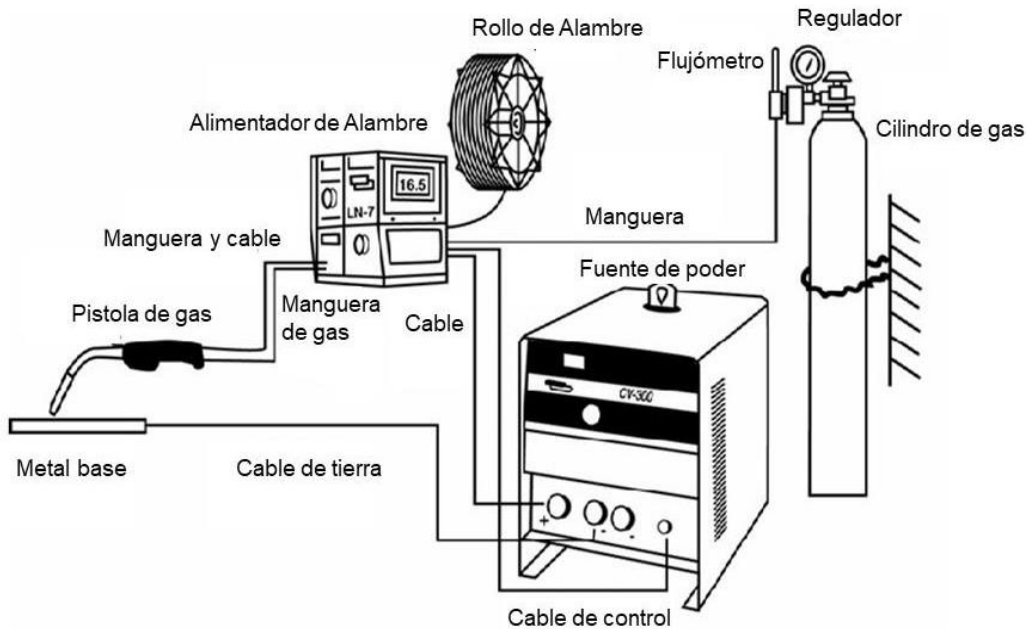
Disposición y partes que integran un sistema de soldadura GMAW
